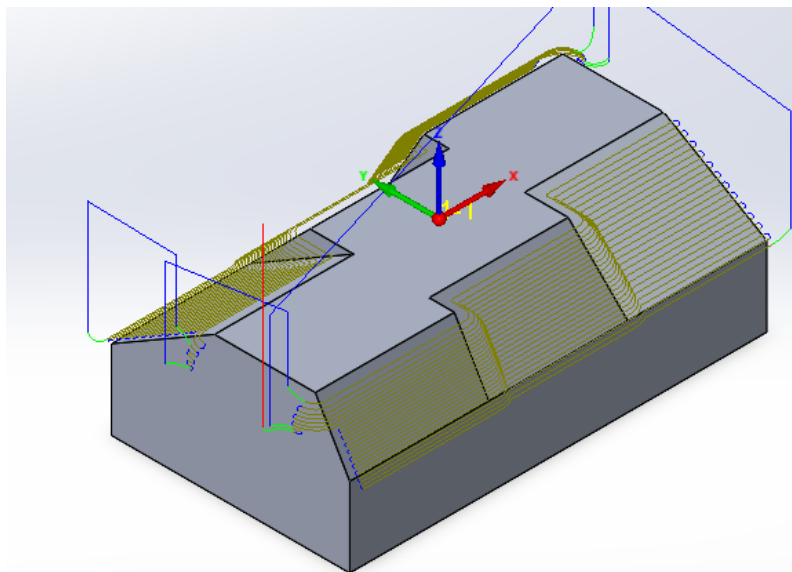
Trajetória executada durante a operação de maquinagem de Z constante turbo
